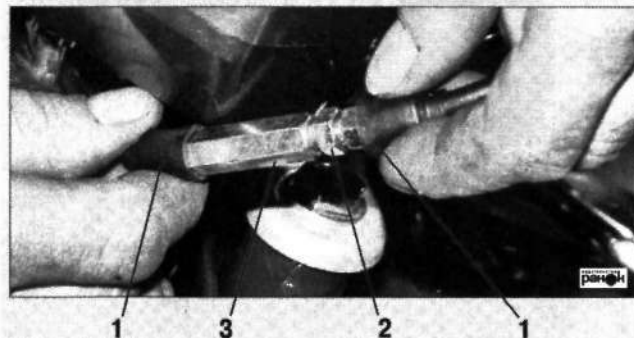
Регулировочная гайка троса акселератора («газа»): 1 — защитный колпачок; 2 — контргайка; 3 — регулировочная гайка троса акселератора («газа»)
